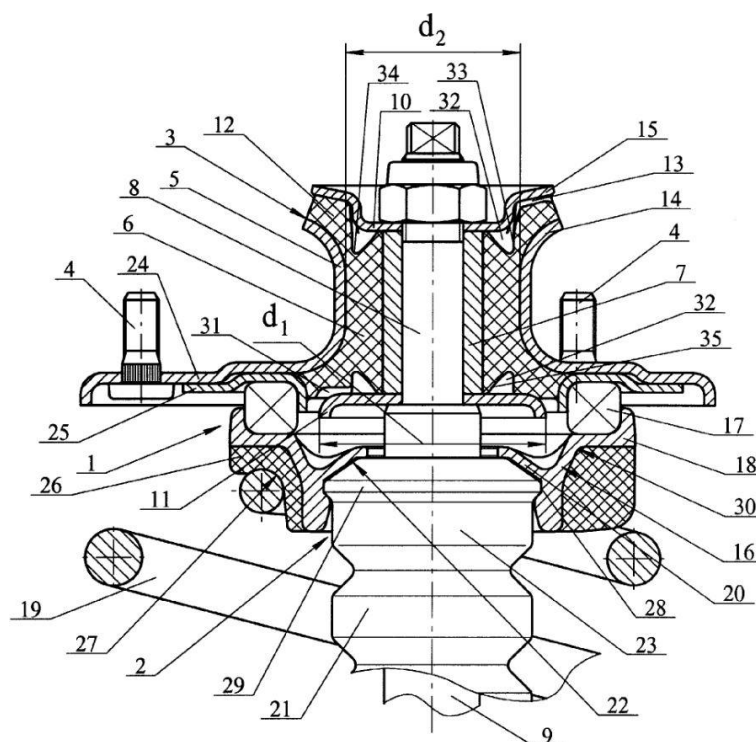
Устройство крепления пружинной стойки подвески автомобиля
